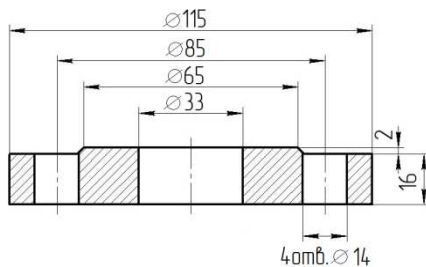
Габаритные и присоединительные размеры фланца\* автоматического газоотделителя
